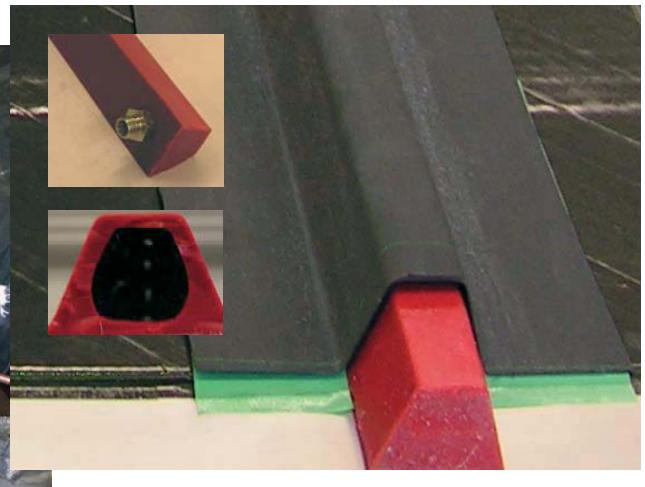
Mehrweg-Elastomer-Formwerkzeugelemente
